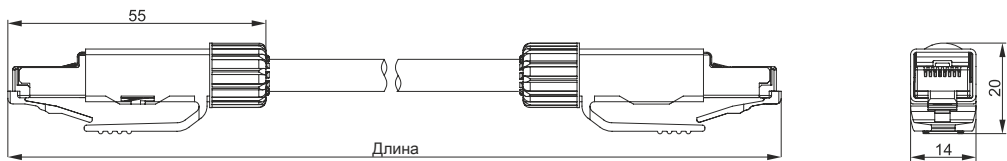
5CASP3.xxxx-00 — Размеры
